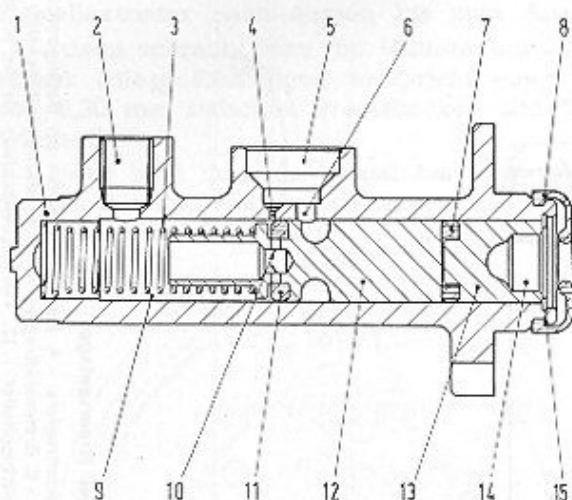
Längsschnitt durch den Hauptbremszylinder.
